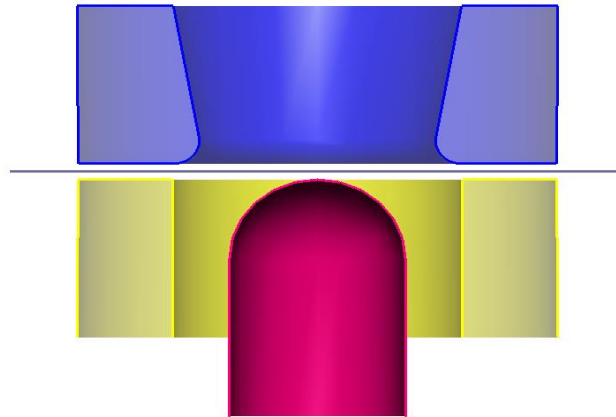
Конечно-элементные модели инструмента и заготовки
